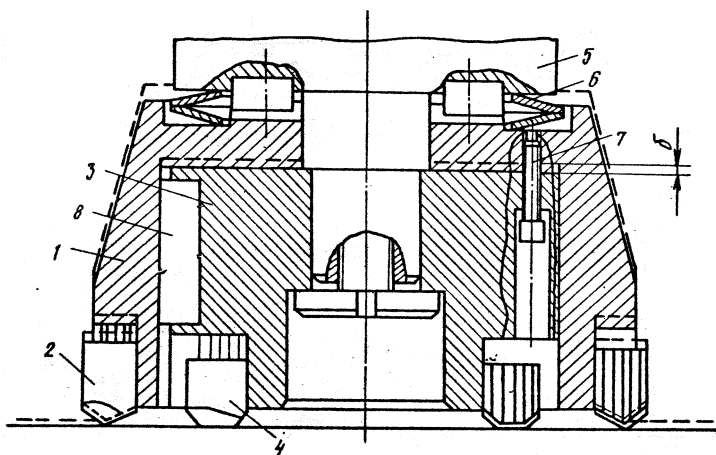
Торцева фреза по а. с. 600757 МКИ В 23 С 5/06
